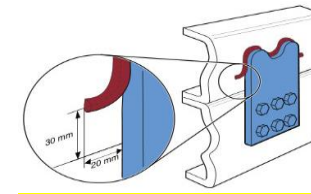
Ejemplo de Soporte rígido soldado y atornillado.
